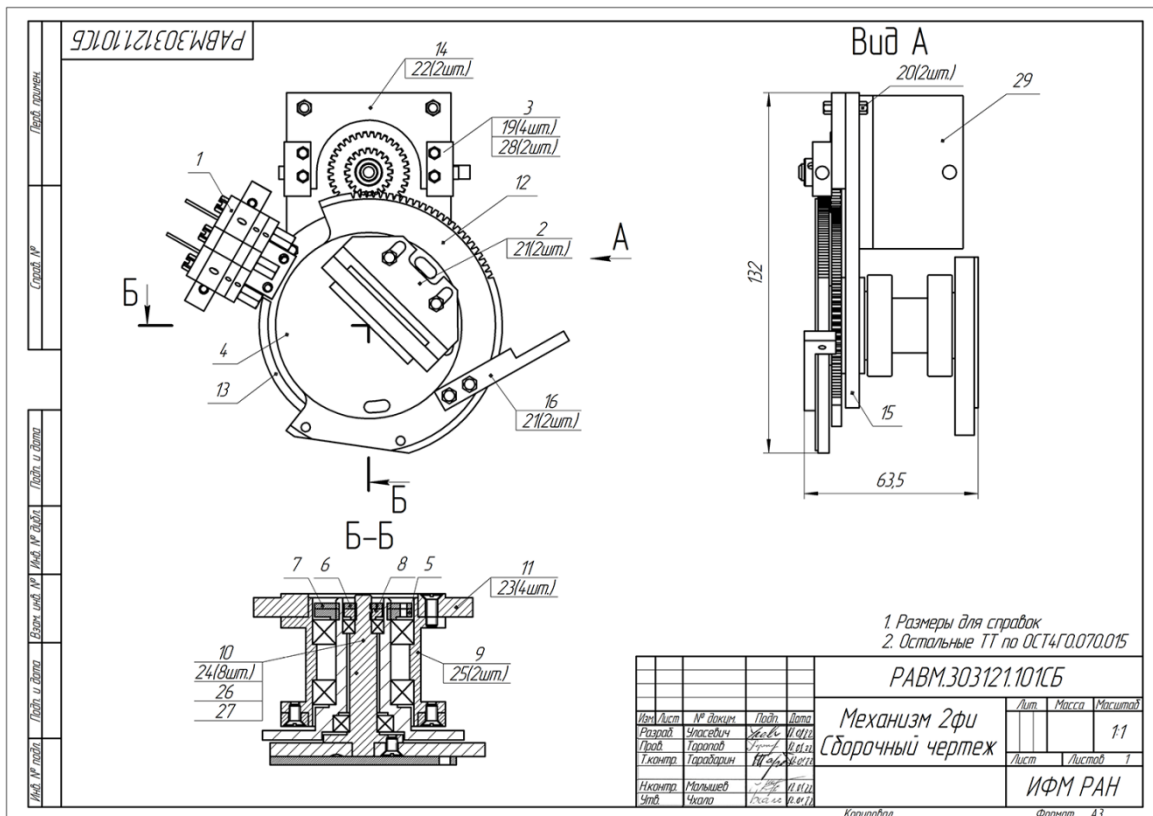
Сборочный чертёж поворотного столика спектрометра МР и ЭУФ излучения
